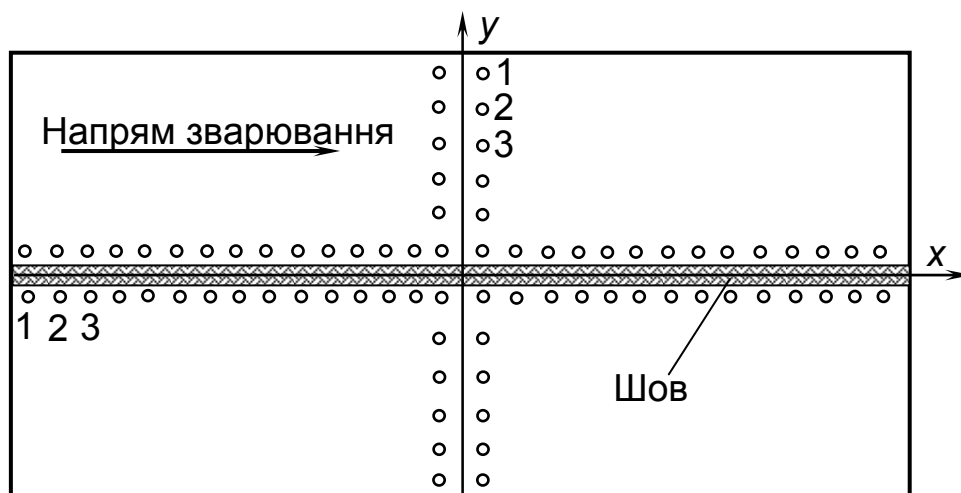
Схема розташування вимірювальних баз на зварному зразку
